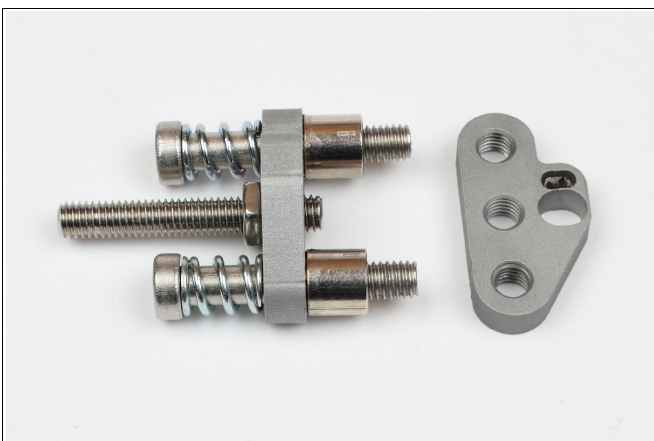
Die Federn werden auf die Schrauben geschoben.
